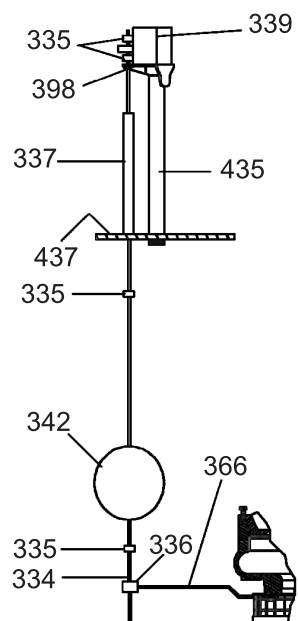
Raggio tra la colonna dell'interruttore galleggiante e il galleggiante.
